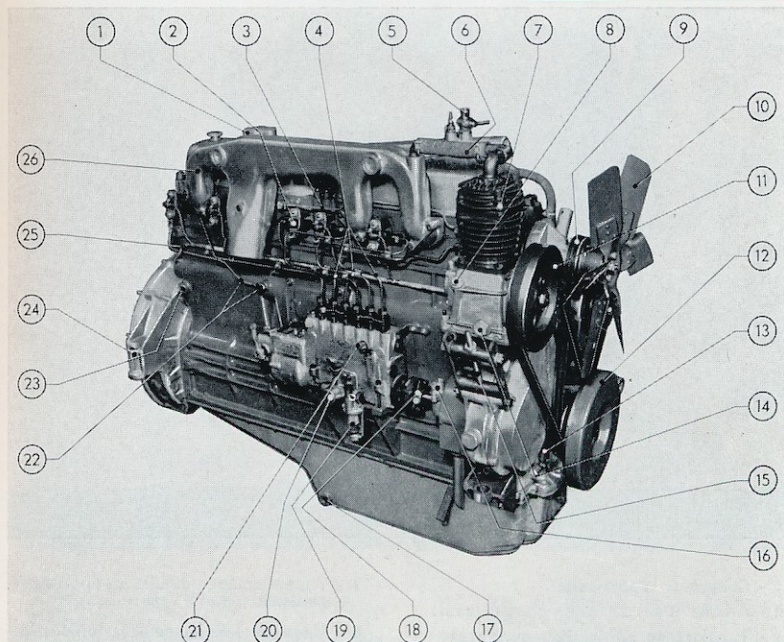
Vue d'ensemble 3/4 droit du moteur 6 cylindres.
